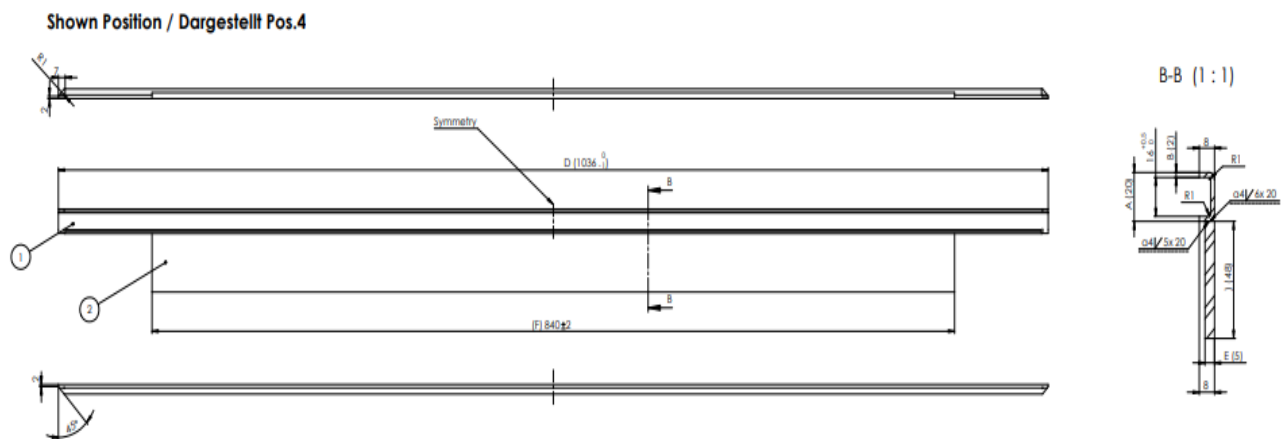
Кресленики зварного елемента бокової рамки з приварним бортом
